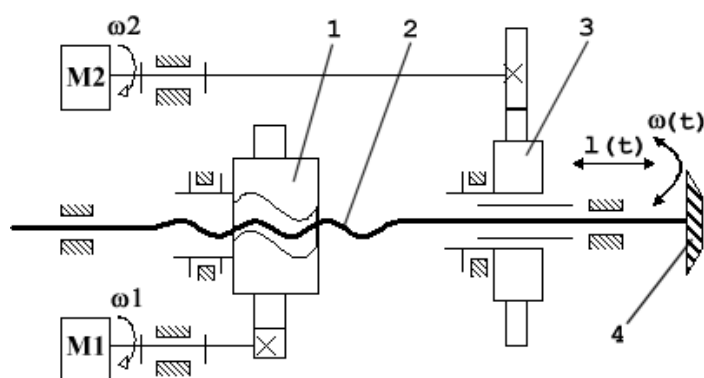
Мехатронный модуль сборки вальцовочных соединений
